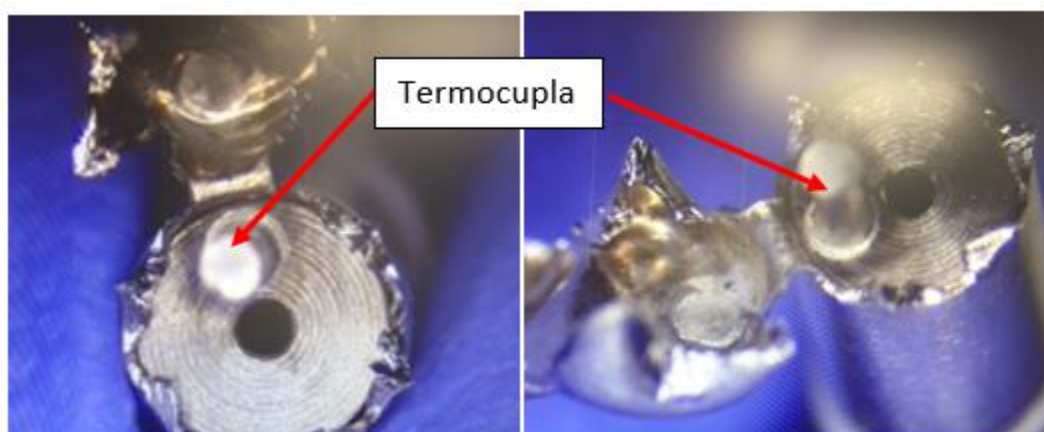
Soldadura entre la termocupla y la pared de la punta
